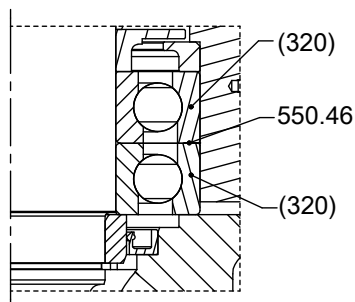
Исполнение подшипника, материал корпуса — высококачественная сталь
